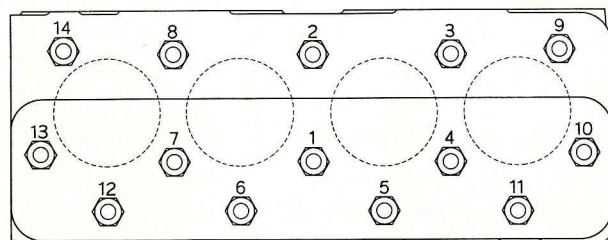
Ordine di serraggio dei dadi per testa cilindri.
